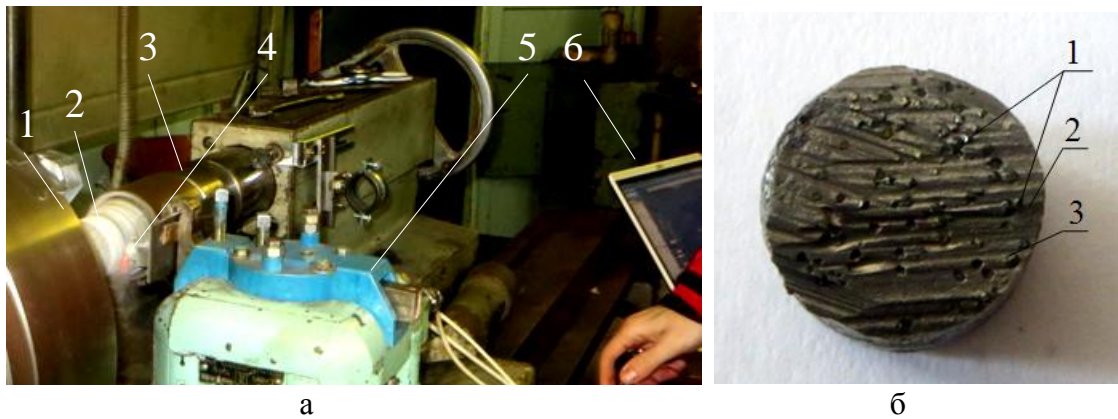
Загальний вигляд експериментального стану, створеного на базі токарно-гвинторізного верстату моделі ДІП-200 : 1–токарно-гвинторізний верстат 2–циліндричний блок пісковика Торезького родовища, 3–оправка для утримання блоку пісковика; 4– циліндричний породоруйнівний елемент, 5 – динамометричний пристрій, 6– дисплей ПЕОМ для реєстрації зусиль руйнування гірської породи–а; породоруйнівного елемента (вид зверху),оснащеного алмазами АС 300Т зернистістю 400/315 мкм : 1– алмазні зерна, 2–матриця із NiSn(6%), 3– мікробороздки на поверхні матричного матеріалу–б
